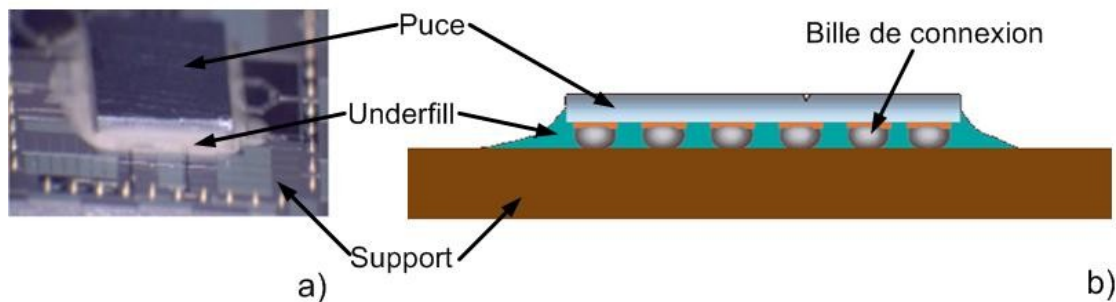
Un assemblage d'une puce active sur un substrat (a) vue de dessus, (b) vue en coupe
